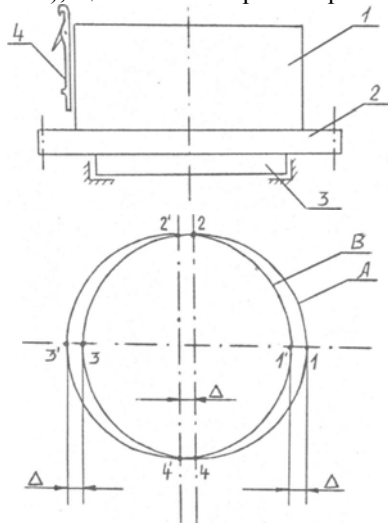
Опора голкового циліндра круглов'язальної машини типу КО: а – схема опори (1 – голковий циліндр; 2 – зубчасте колесо; 3 – опорна частина циліндра; 4 – голки); б – траєкторія руху голок (вигляд зверху): А – в початковий період роботи; В – при зношенні опори
